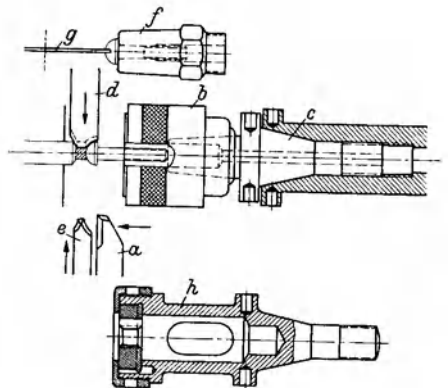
Bearbeitung einer Halbrundkopfschraube.
